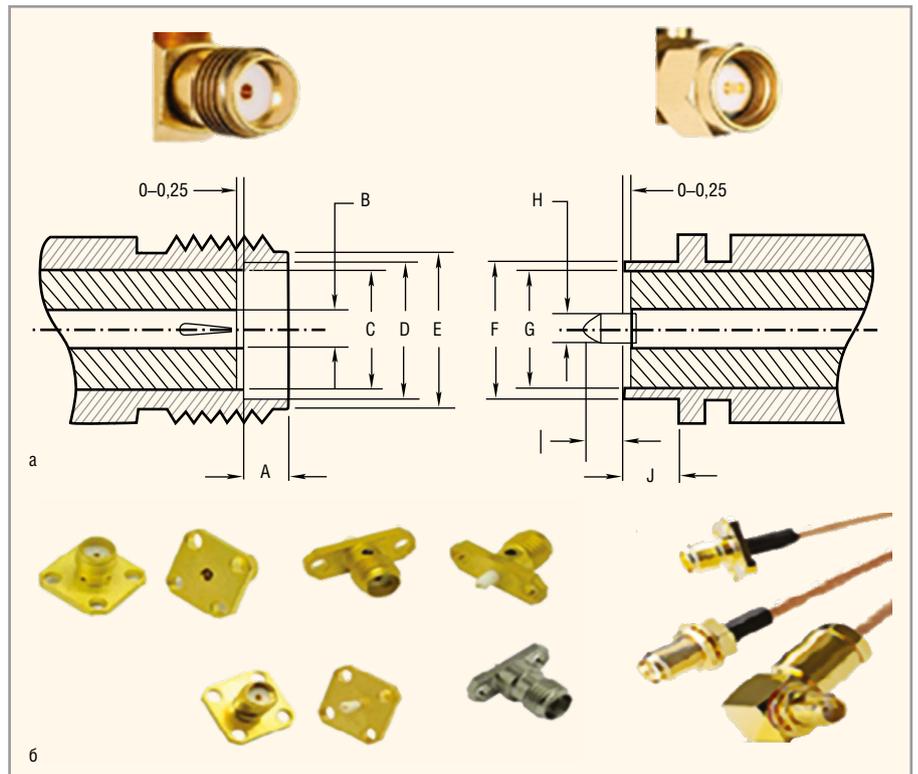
Соединители SMA: а – интерфейс; б – внешний вид
